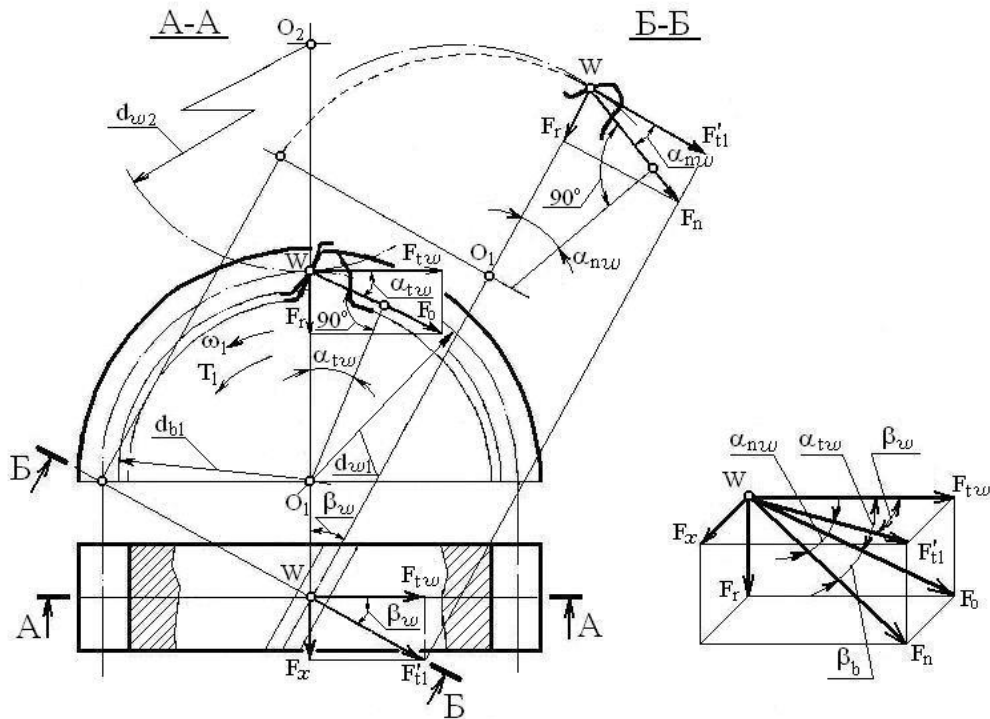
Силы в зацеплении цилиндрических колес с эвольвентным профилем зуба
